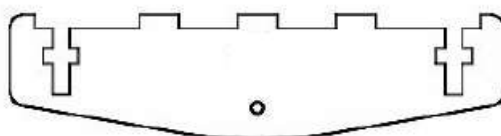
Права бокова частина вертикальної платформи
